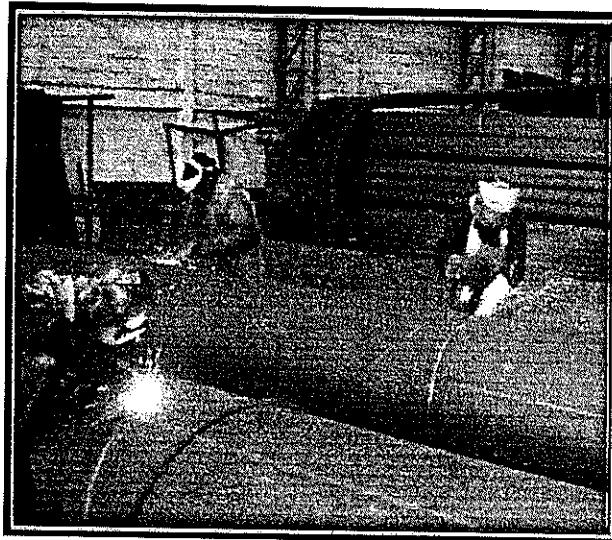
PROCESO DE SOLDADURA CON PROCESO MIG PARA ENSAMBLAJE DE TRAMOS NODULARES PARA HACER SEGMENTOS LARGOS DE 6 M.
